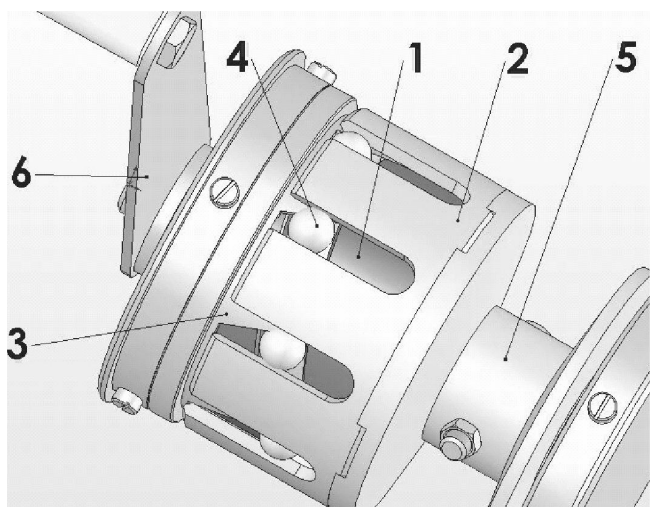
Конструкция редуцирующего узла лебедки. 1 – внутренний кулачок; 2 – вал с пазами; 3 – наружный кулачок; 4 – тела качения; 5 – барабан; 6 – рукоятка.
